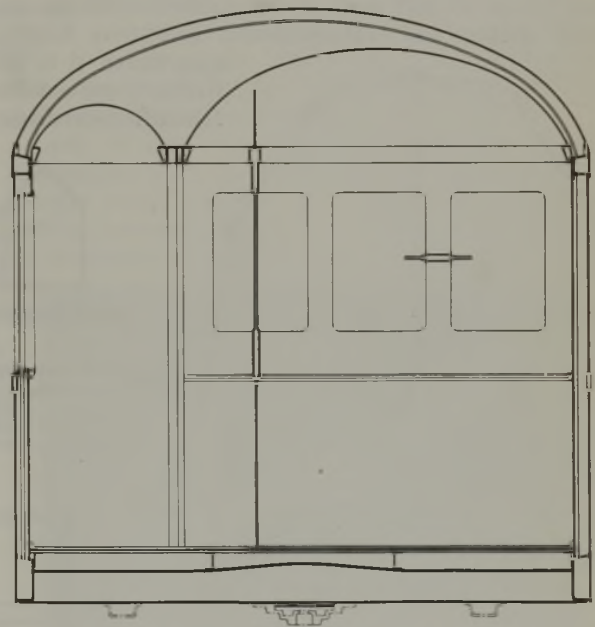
Querschnitt eines geschweißten D-Zug-Wagens.
